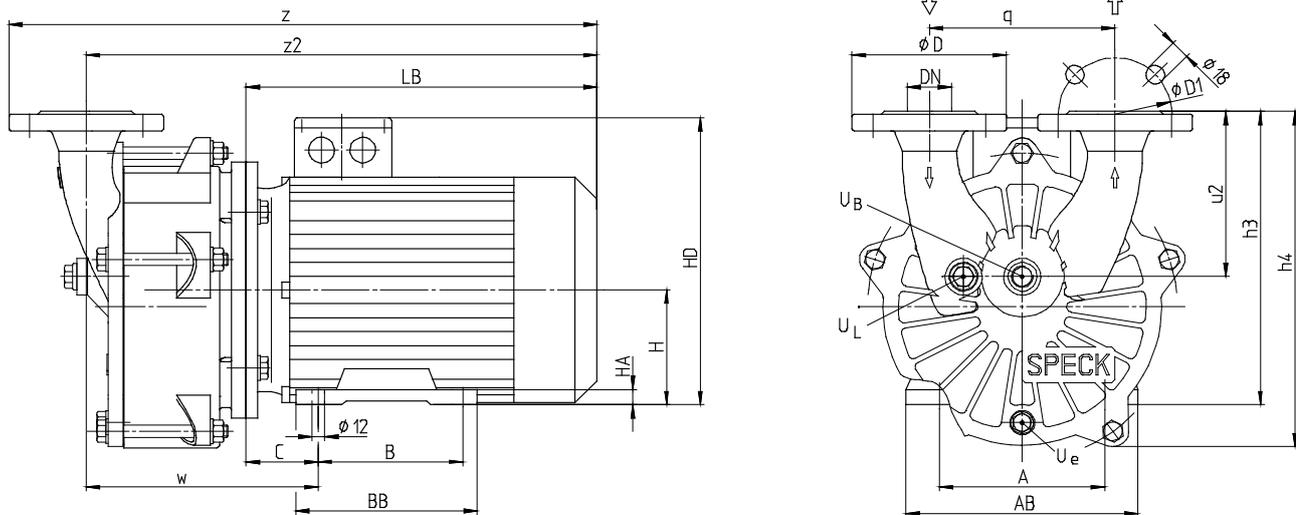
Maßzeichnung VG-95/130/155/255 – Flanschausführung
